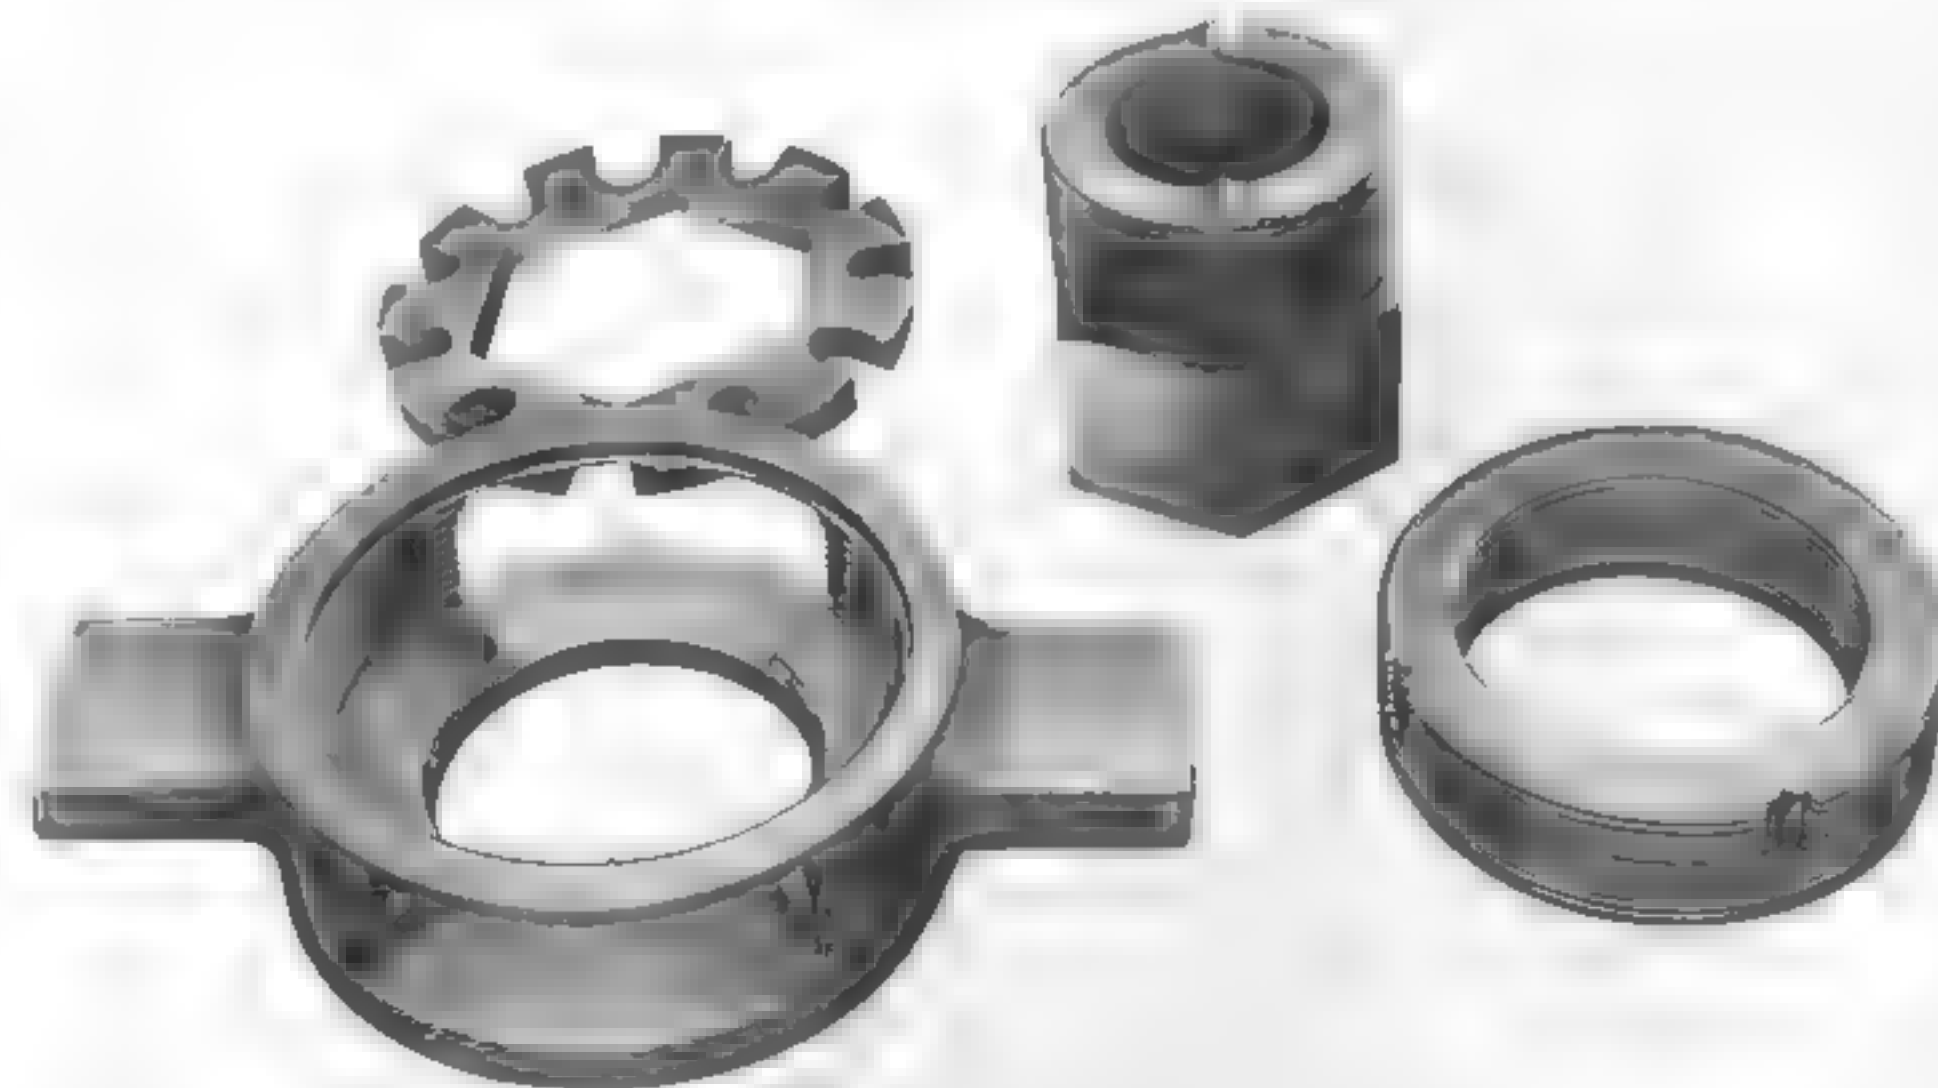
Das Gerät: unten links = Gewindeflansch für mittleren Bombenbodenzapfen, unten rechts = Einsatzstück für kleinen Bombenbodenzapfen, oben rechts = Sechskantschlüsselstück (mit Linksgewinde) mit Rastnasen für die Schlüsselnuten an der Buchse, oben links = Mitnehmerscheibe. (Die nun folgenden Bilder veranschaulichen den weiteren Vorgang lediglich an der Bombe ohne Zünder)
